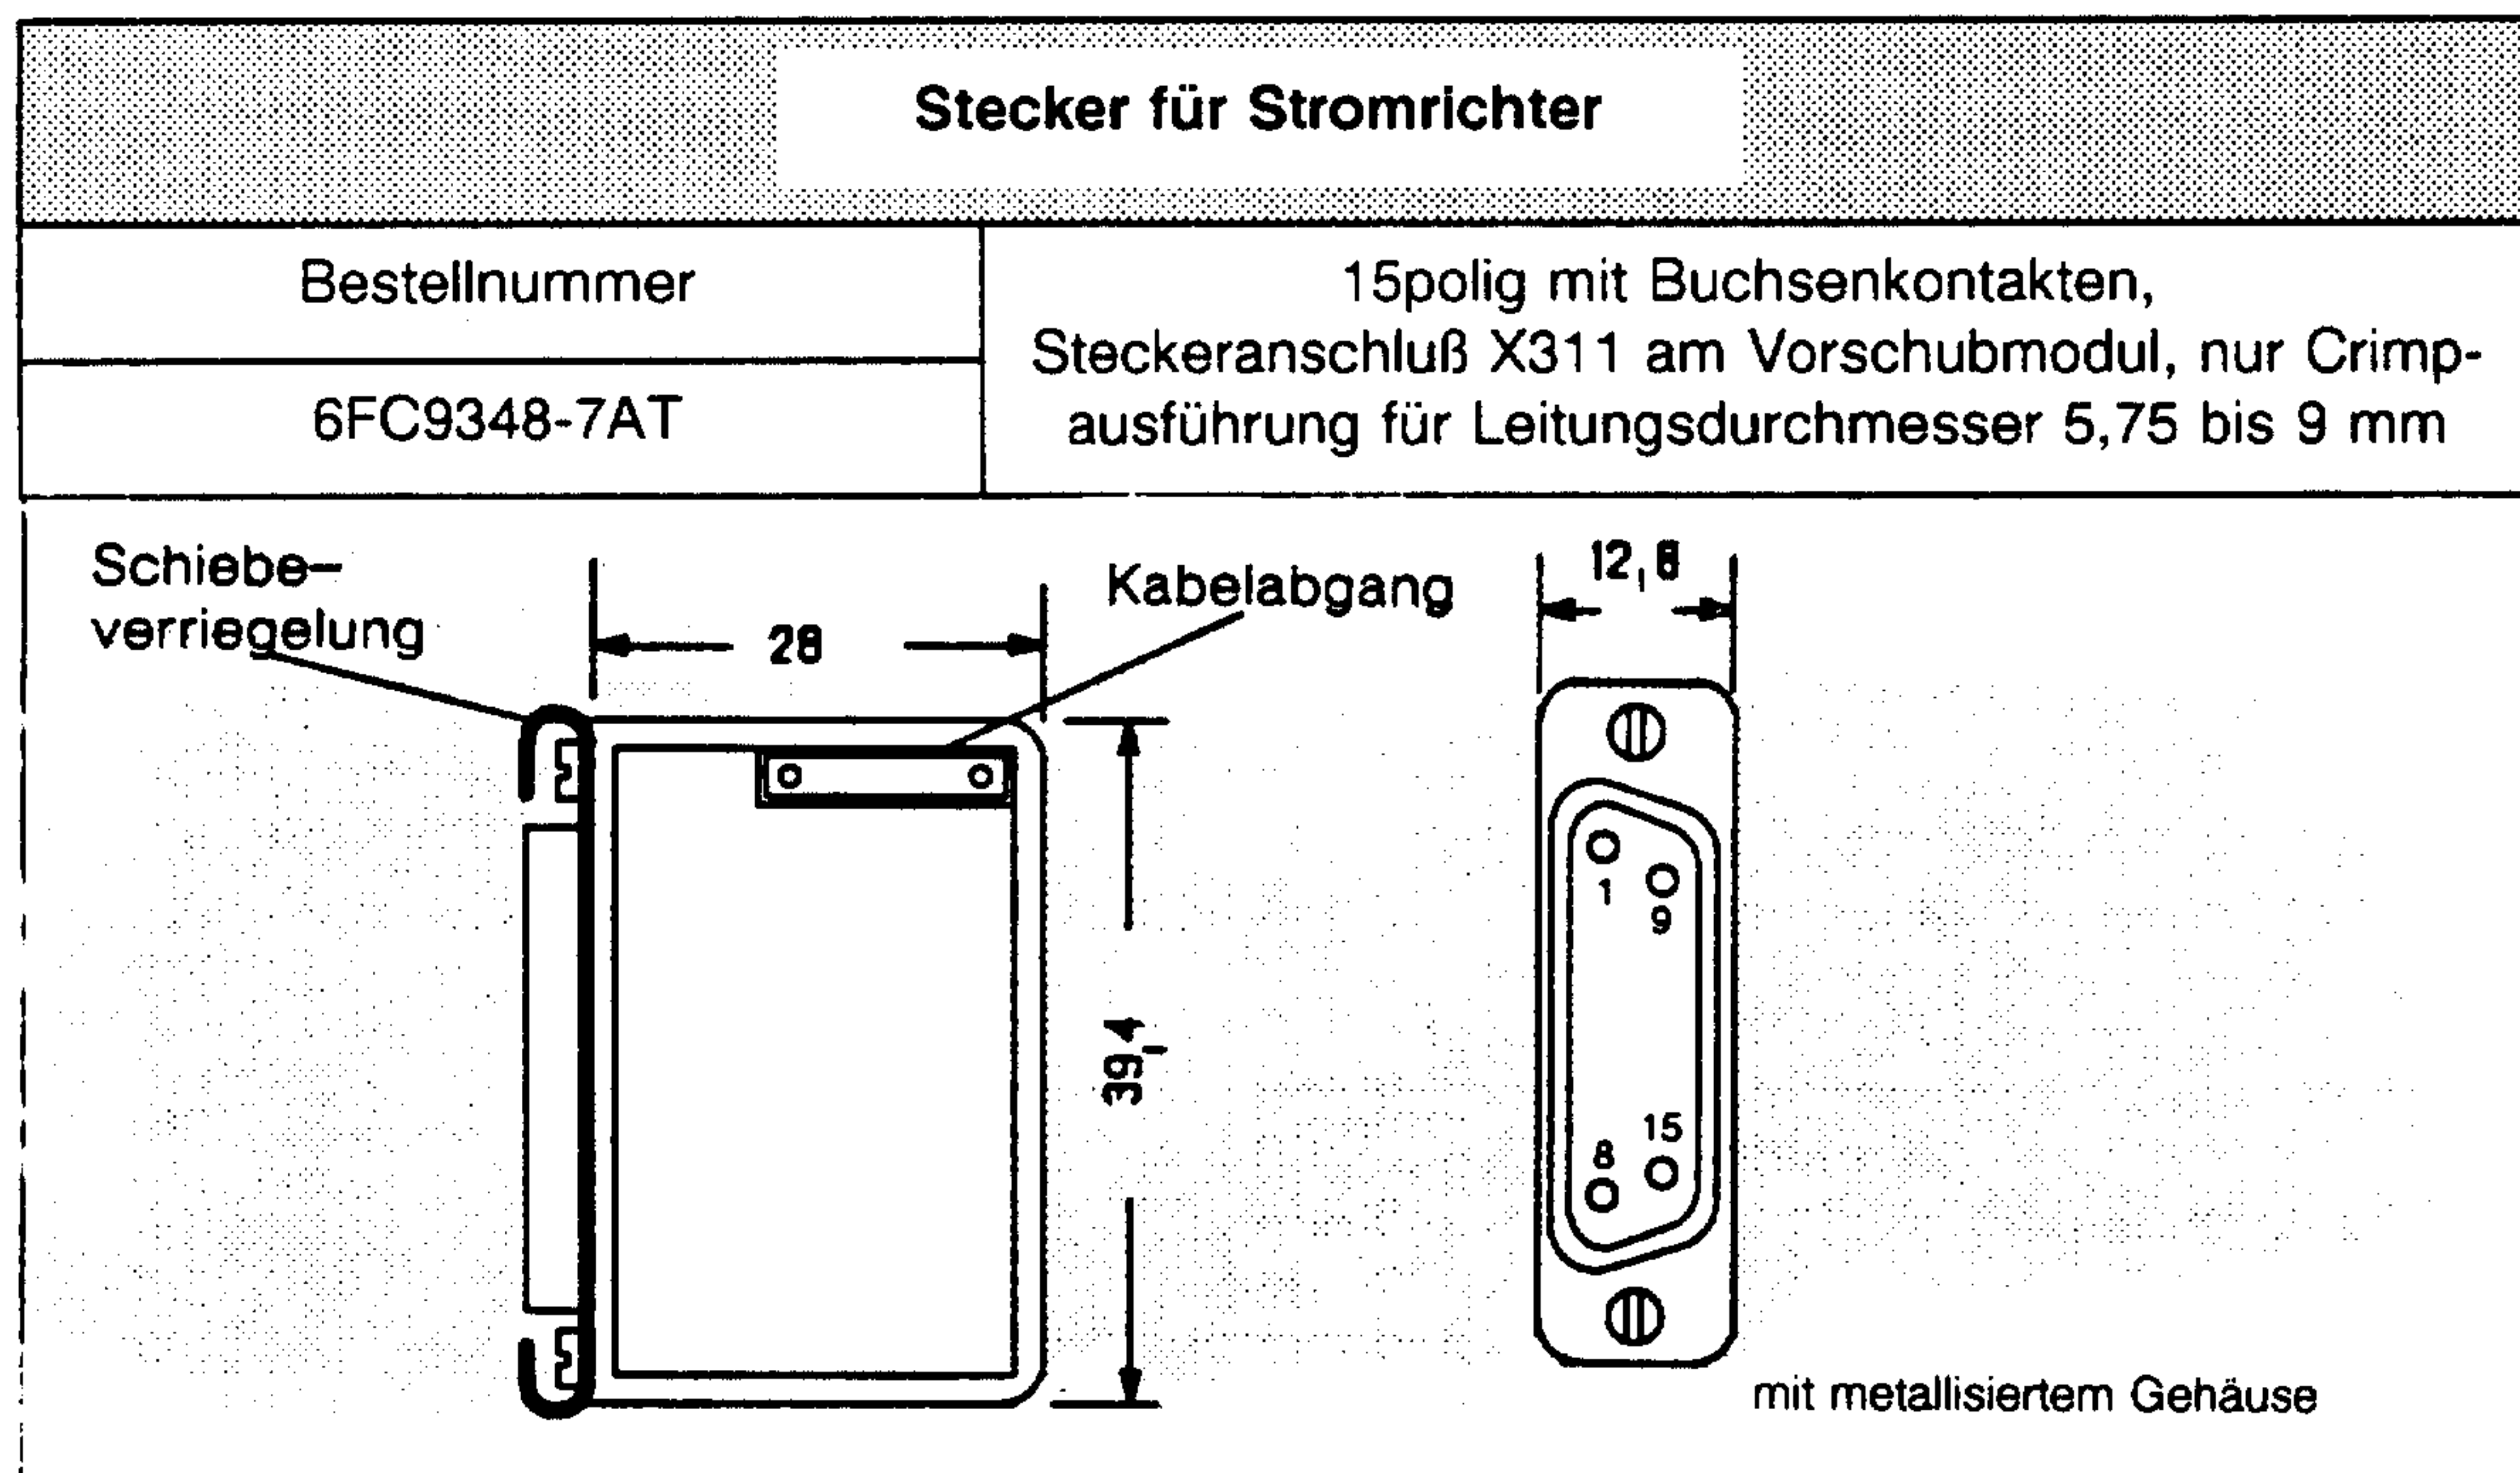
Stecker mit metallisiertem Gehäuse für den Anschluß an den Pulsumrichter SIMODRIVE 611
